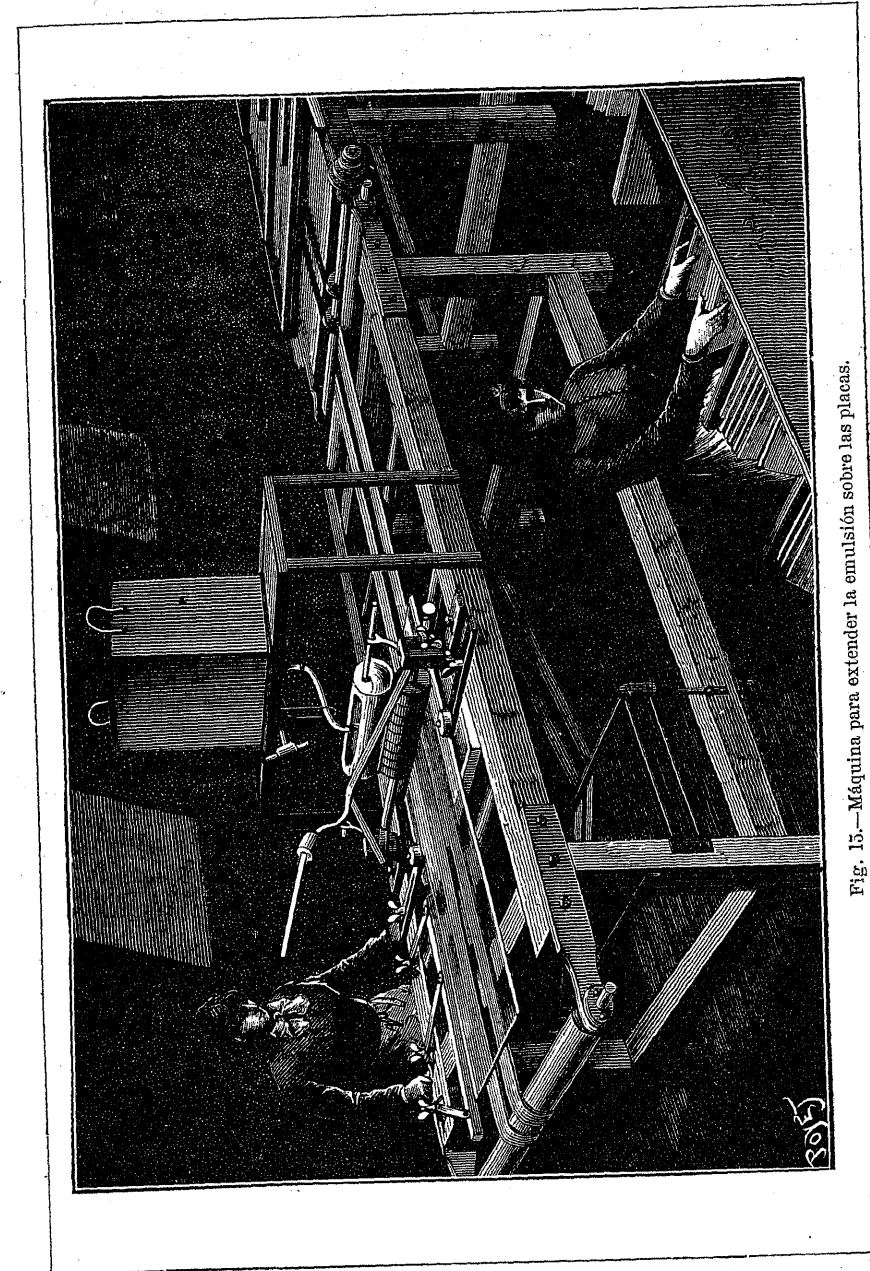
Máquina para extender la emulsión sobre las placas.
